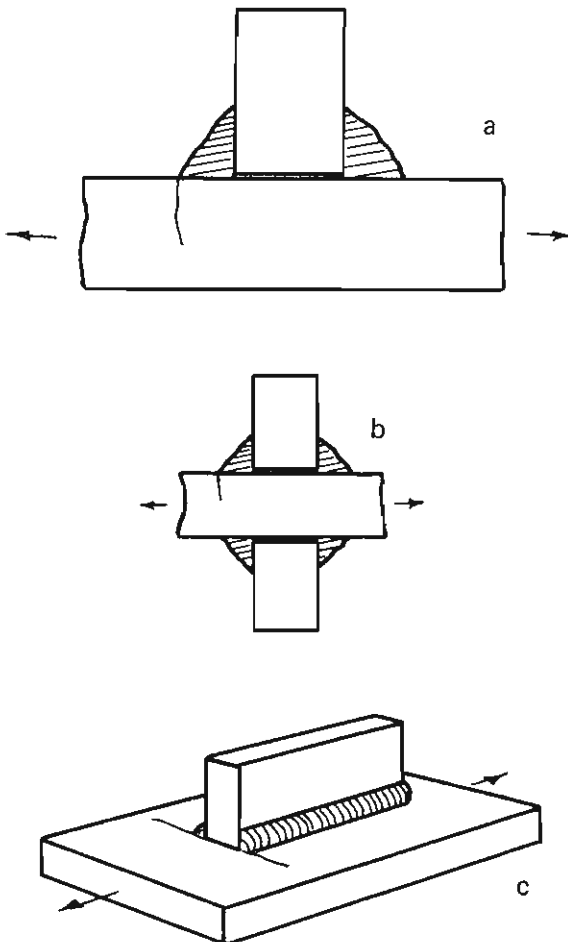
Fissuration par fatigue d'une soudure en croix à âme continue.
